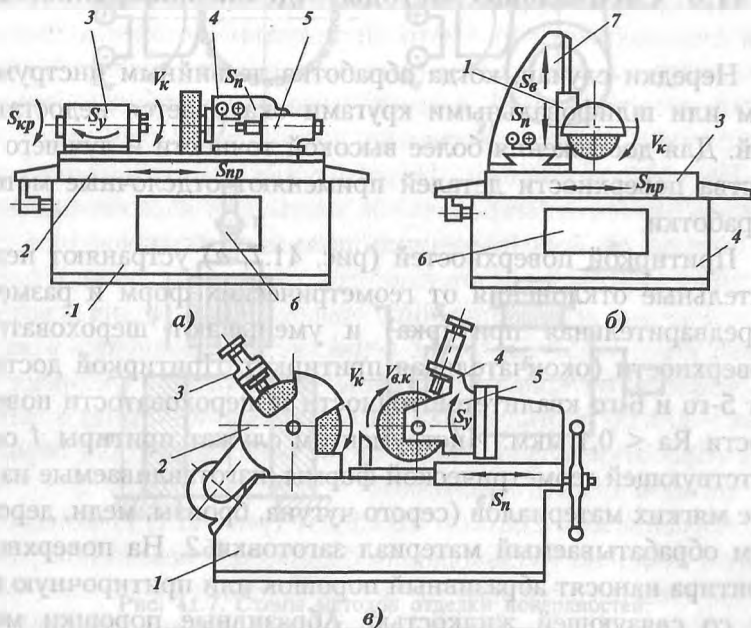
Общие виды шлифовальных станков: а — круглошлифовальный; б — плоскошлифовальный; в — бесцентрово-шлифовальный
